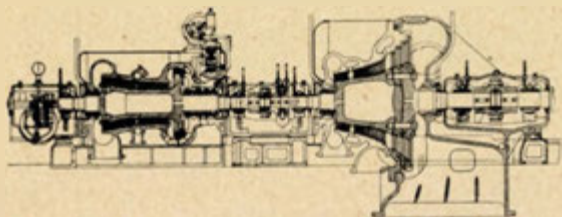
Č. K. D. Podélný řez první turbinou 14.000 kW, 3.000 ot./min.
